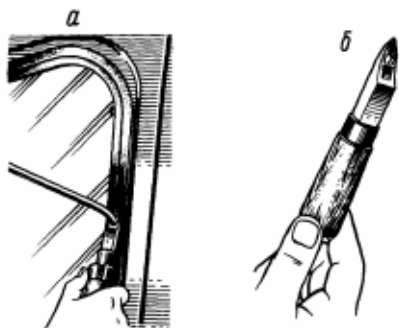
Установка замочного вкладыша при помощи оправки:
